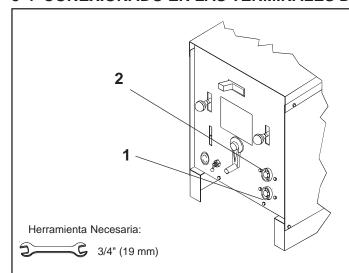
Conexión a Tierra de la Máquina Soldadora.
